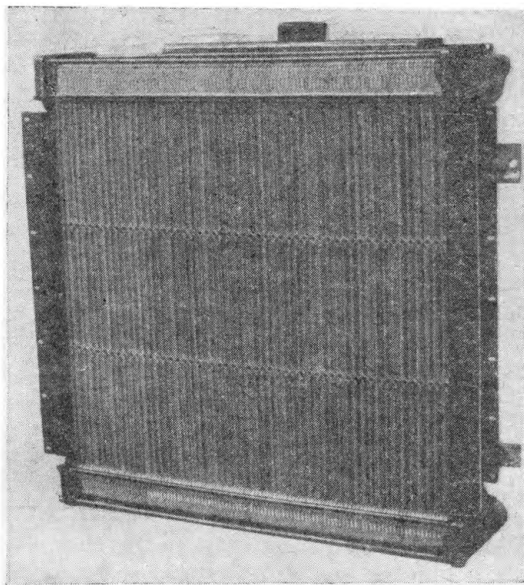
Секция радиатора отопителя, изготовленная холодной прессовой сваркой.
